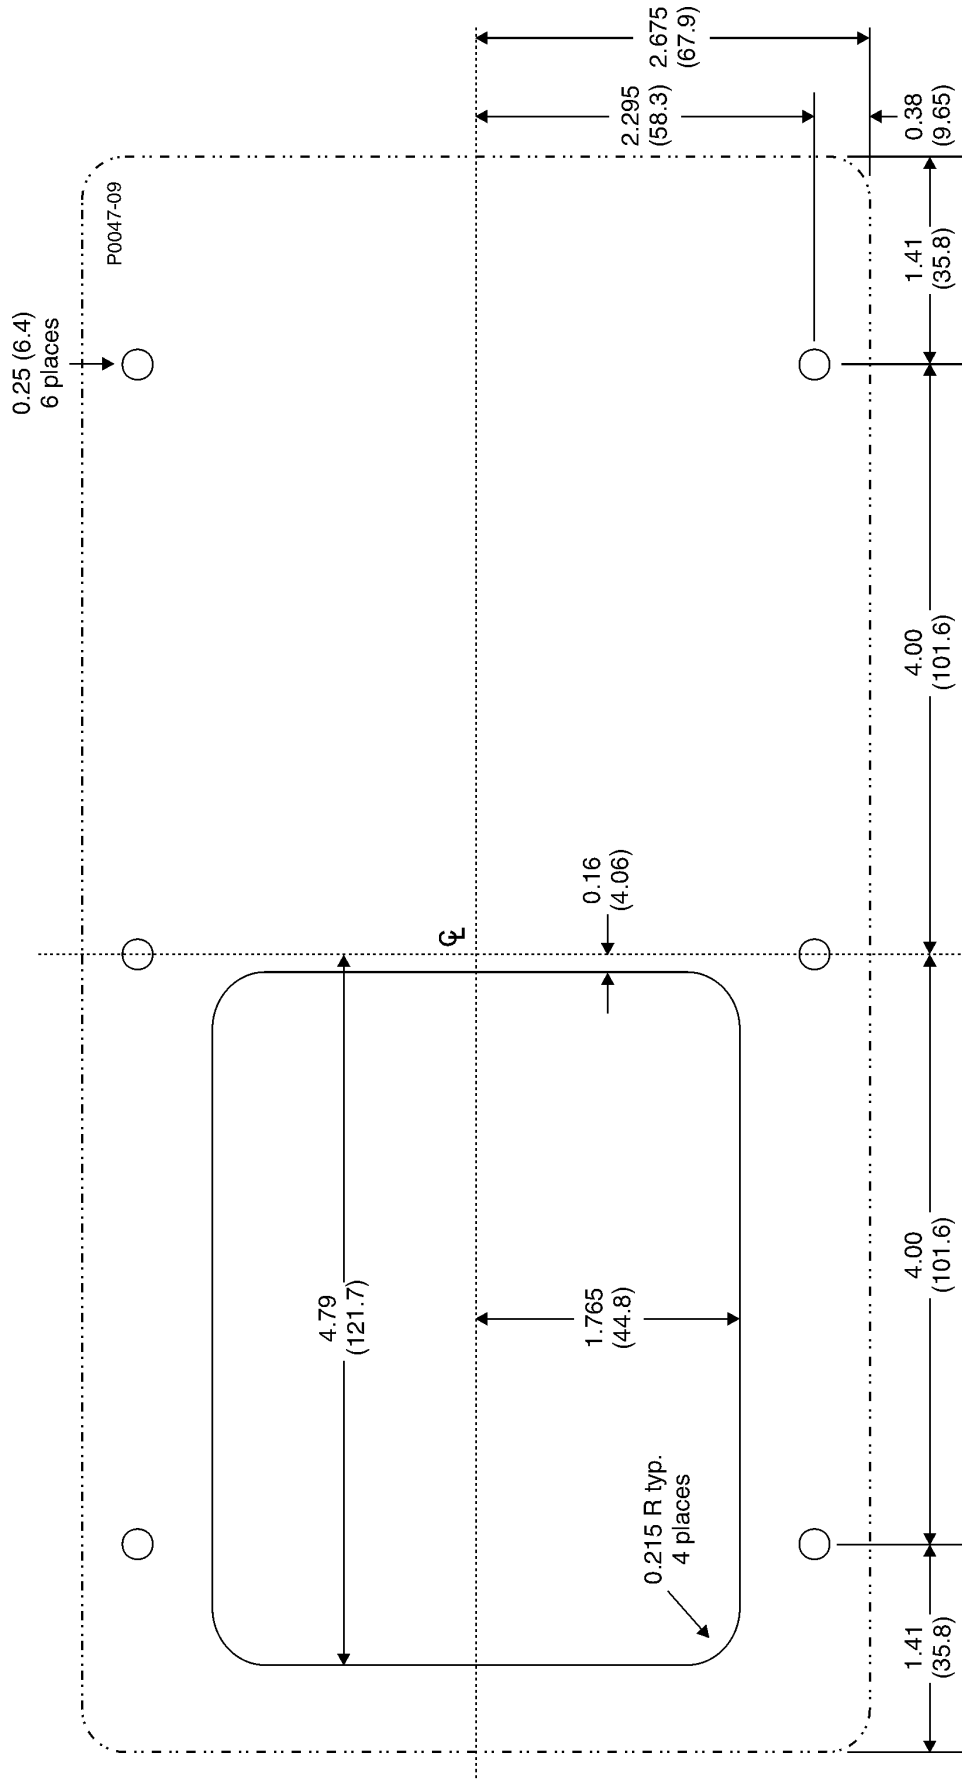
Dimensions de découpe et de perforations, PIN E000-23801
